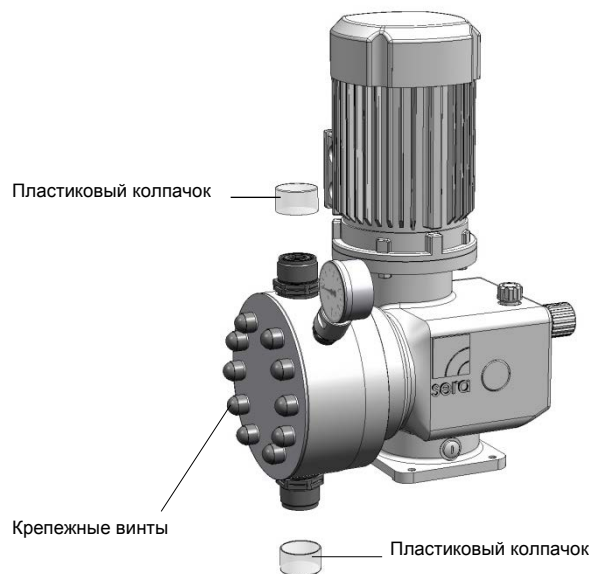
Многослойный мембранный насос с пластиковыми колпачками
